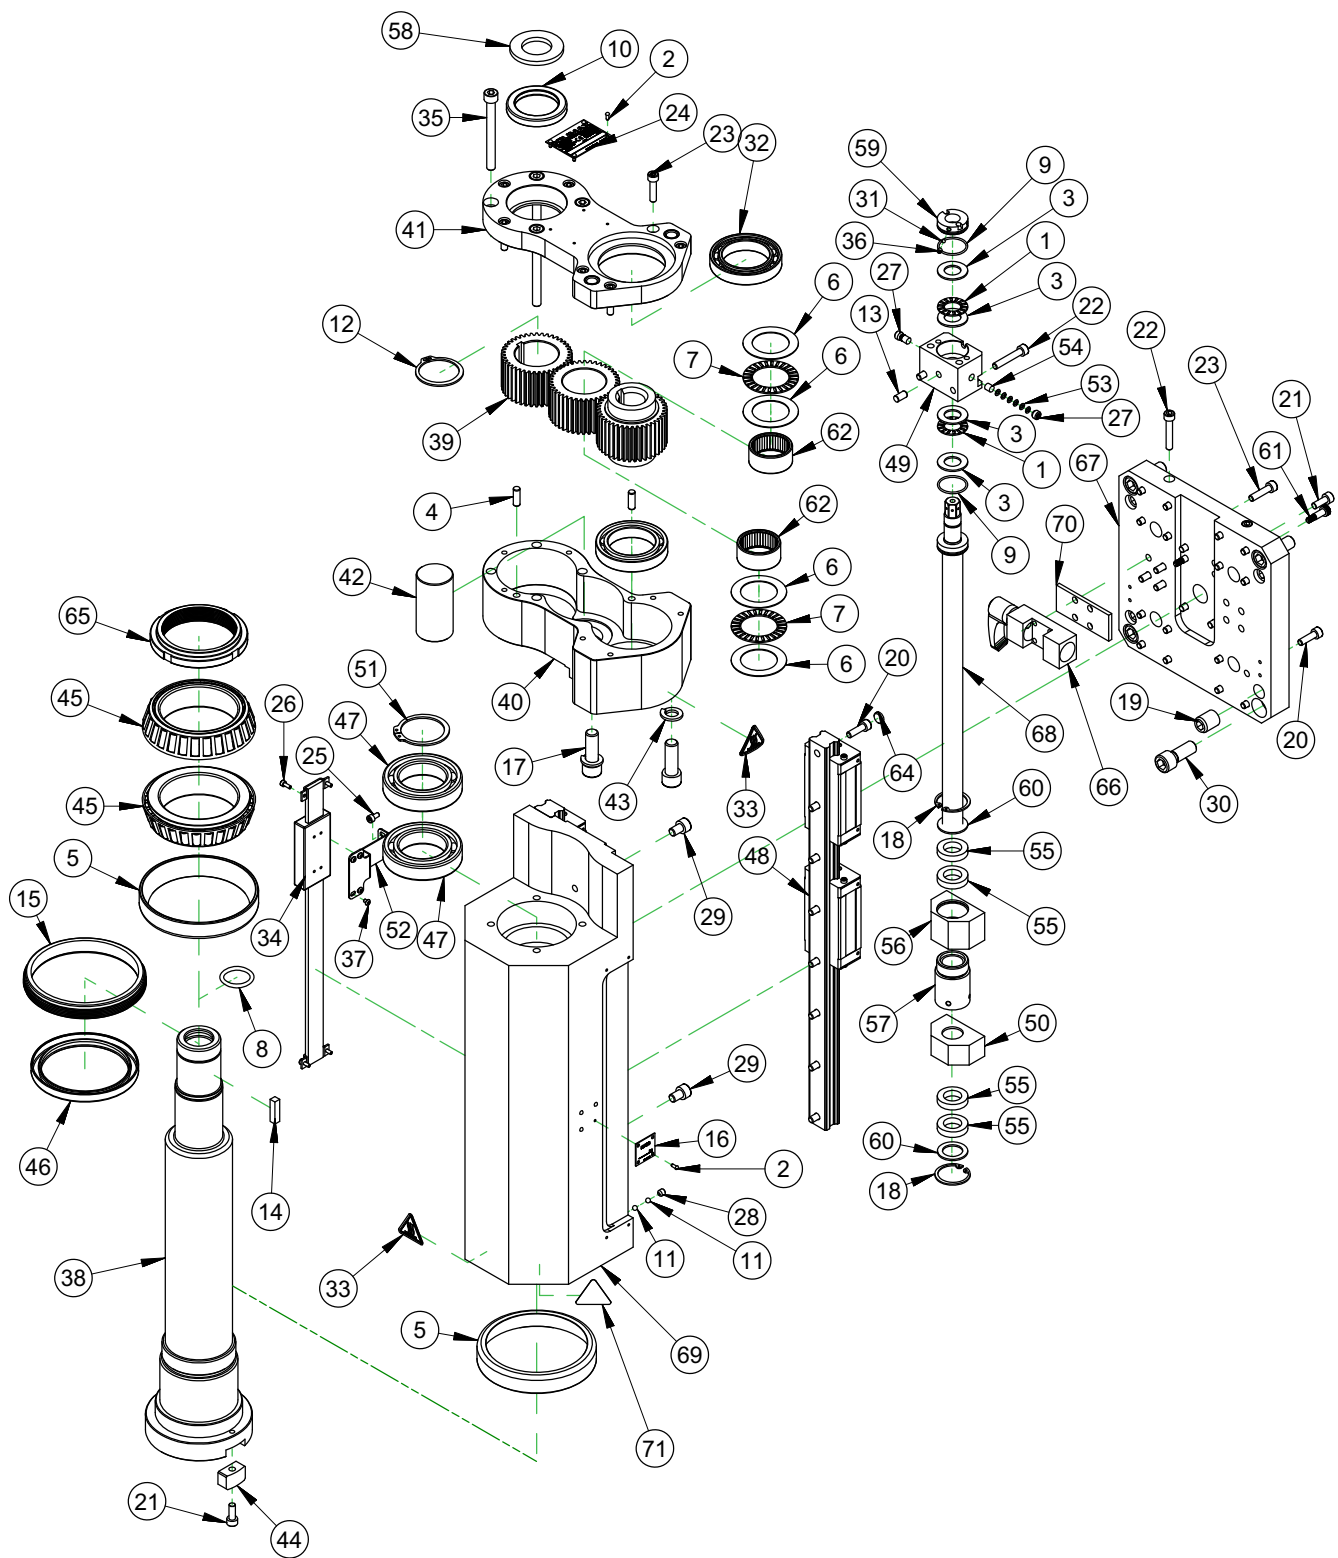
ФРЕЗЕРНАЯ ГОЛОВКА 2-29/32 с подшипником 8, ход #50 конусная (P/N 72277)
